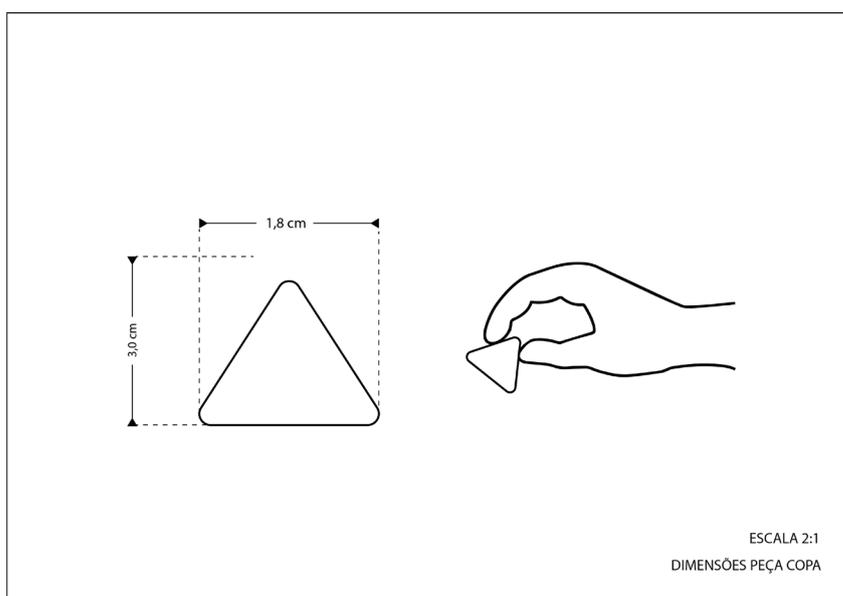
Vista frontal desenhada com dimensões das peças copa.
